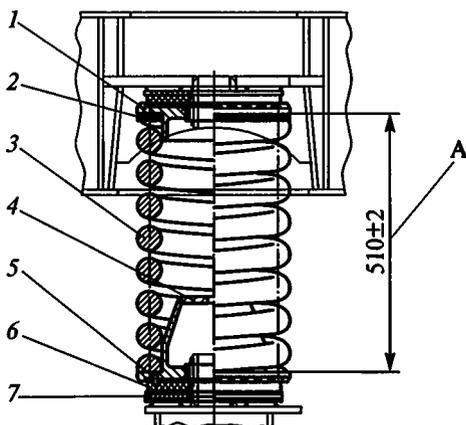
Опора рамы кузова на крайние тележки типа «Флексикоил»: 1 — опора верхняя; 2 — шайба; 3 — пружина; 4 — опора нижняя; 5 — винт; 6 — шайба; 7 — полукольцо
